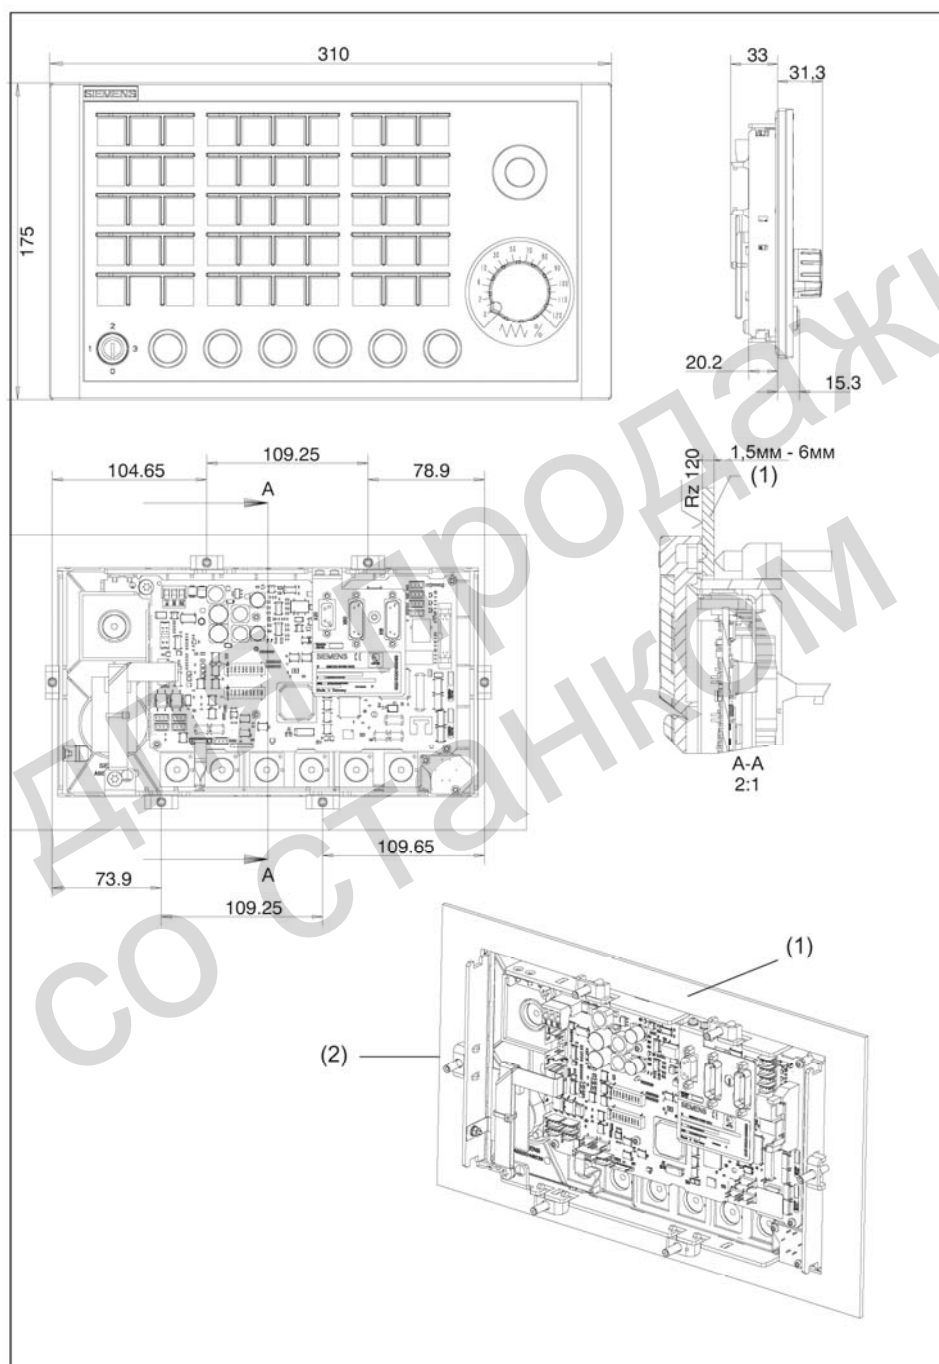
Габаритный чертеж станочного пульта МСР 310
